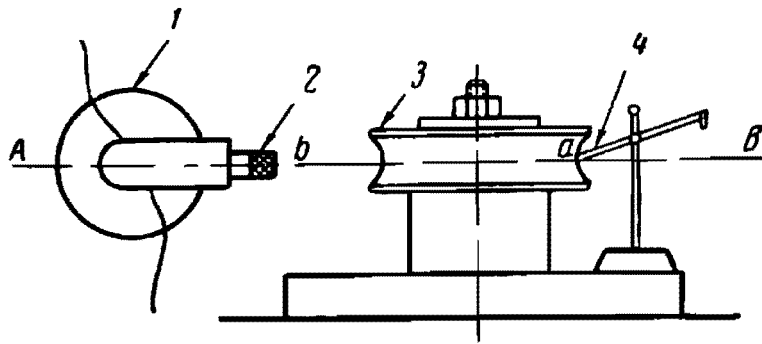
Установка червячной фрезы при нарезании червячного колеса
